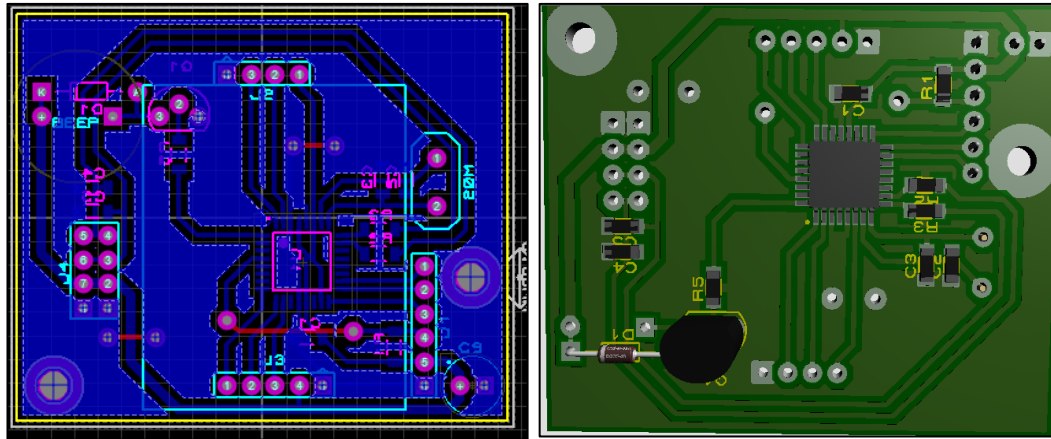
Diseño de placa de Control programa Proteus PCB layout y 3D Visualizer
